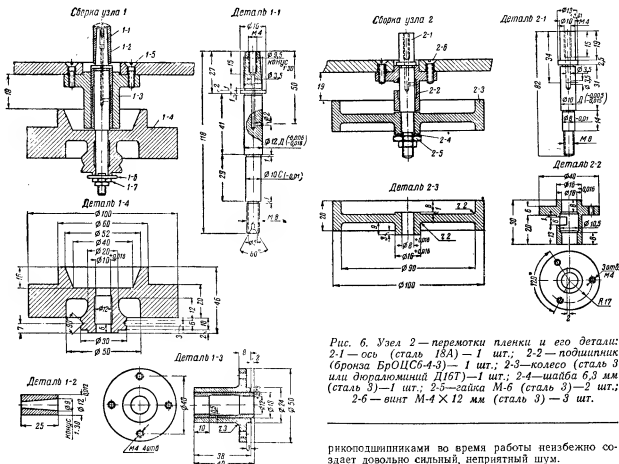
Ведущий ролик (тонвал) с маховиком (узел 1) и его детали: 1-1 — ось (сталь У8А) — 1 шт.; 1-2 — насадка (сталь У8А) — 1 шт.; 1-3 — подшипник (сталь 3) с запрессовкой бронзового вкладыша (БРОЦСб-4-3) — 1 шт.; 1-4 — маховик (сталь СЧ-21-40) — 1 шт.; 1-5 — винт М4×15 мм (сталь 3) — 4 шт.; 1-6 — шайба 8,5 мм (сталь 3) — 1 шт.; 1-7 — гайка М-8 (сталь 3) — 2 шт.
